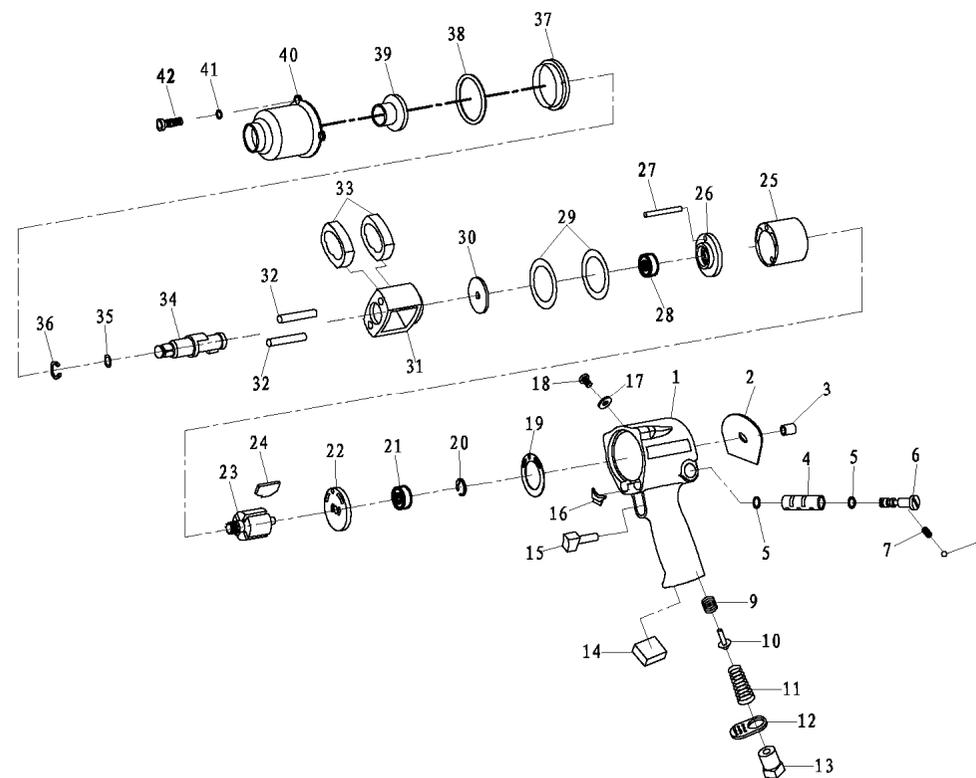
а. Схема устройства и сборки гайковерта ручного пневматического MFW 016/610-1.
